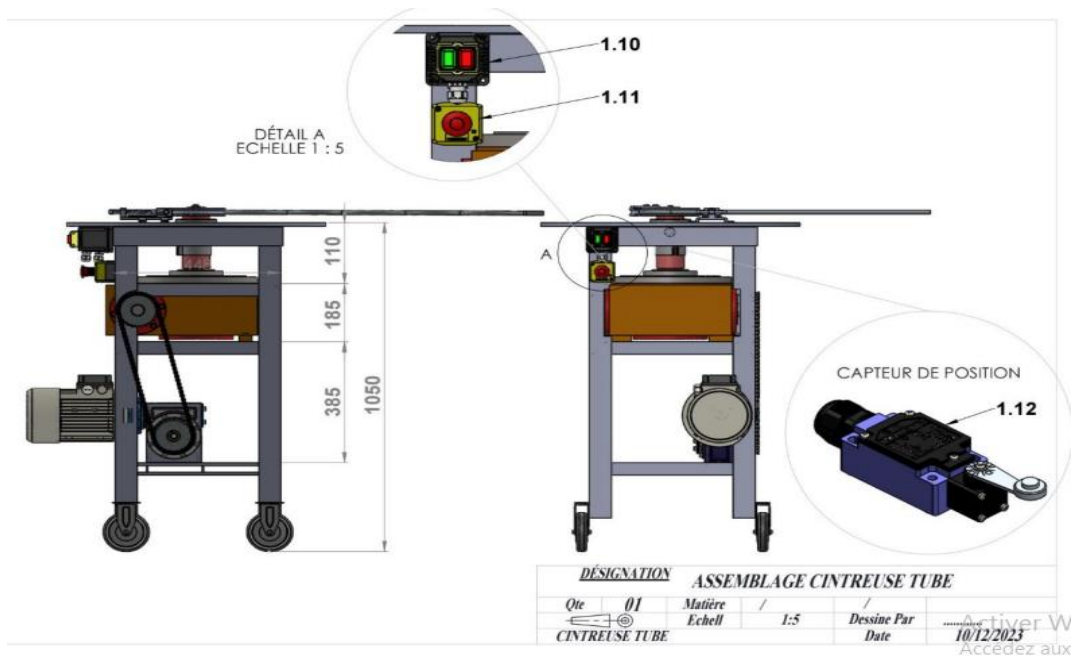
(b): Vue de face - vue d'arrière de l'assemblage de la cintreuse plane
